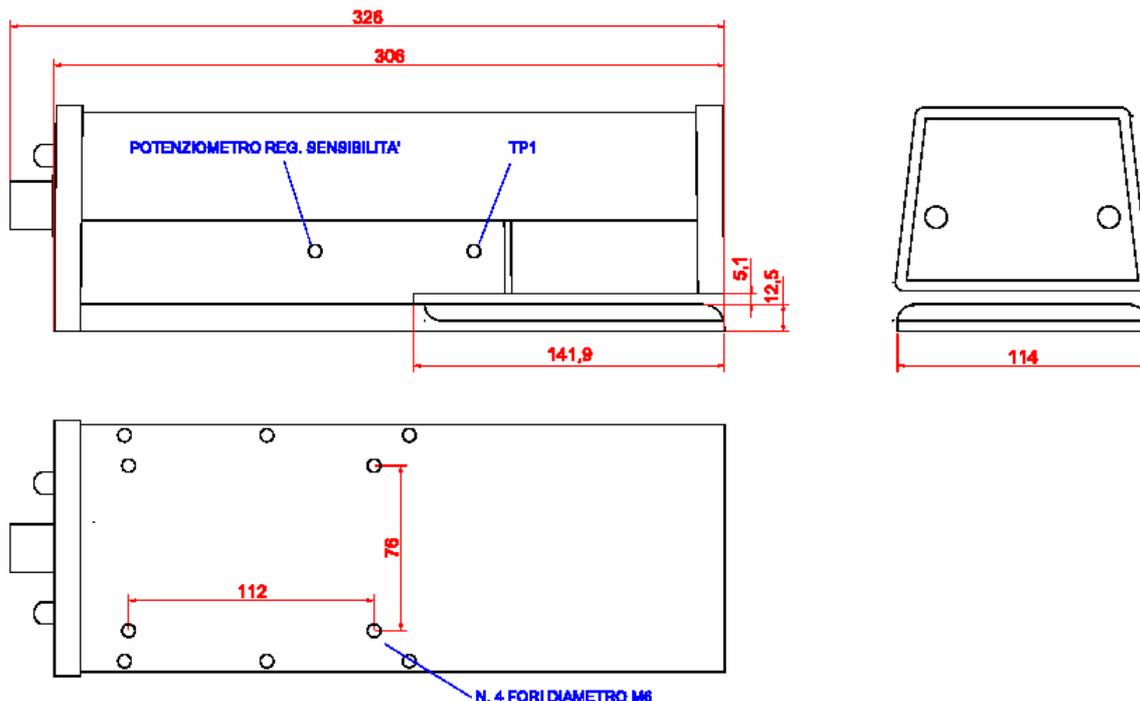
Dimensioni di ingombro e installazione Rilevatore Giunte
